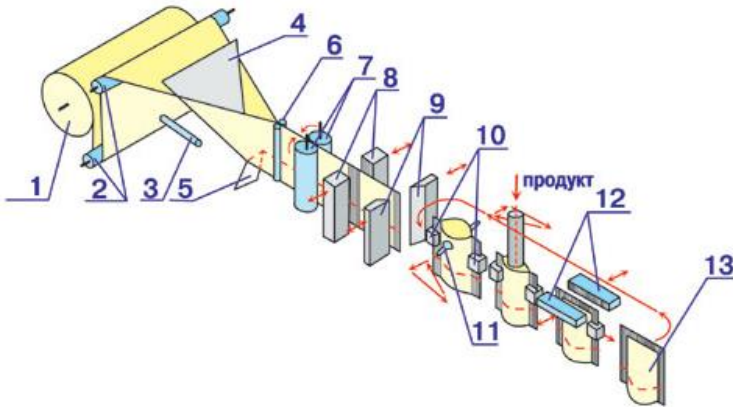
Технологічна схема пакування в пакети “дой-пак”: 1 – рулон; 2 – ролики натяжні; 3 – пристрій нанесення термоклею; 4, 5 – формуючі елементи; 6 – ролики притискні; 7 – ролики протяжні; 8 – губки поздовжнього зварювання; 9 – ножі; 10 – захвати; 11 – пристрій розкриття пакету; 12 – губки поперечного зварювання; 13 – готовий пакет
